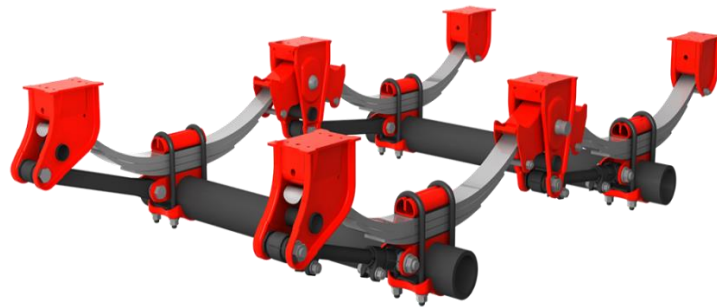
Diseño 3D suspensión Hutch 9700. Fuente: hutchensindustries.com
